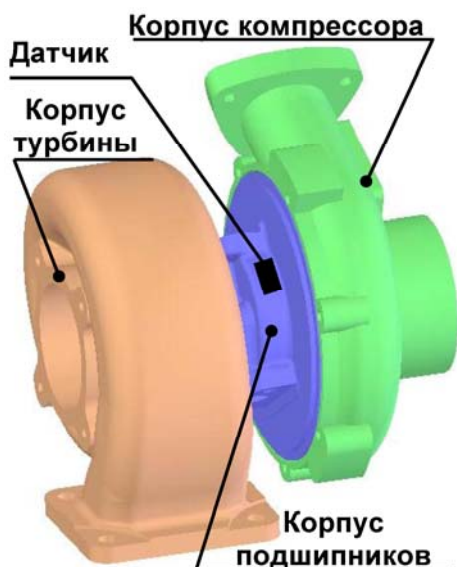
Схема установки датчика виброускорений на корпусе ТК
